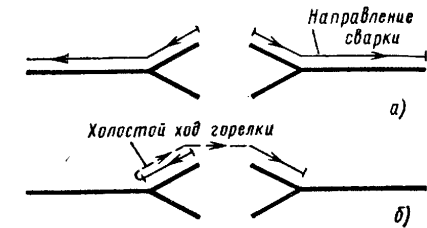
Схема движения головок при сварке корневых швов
